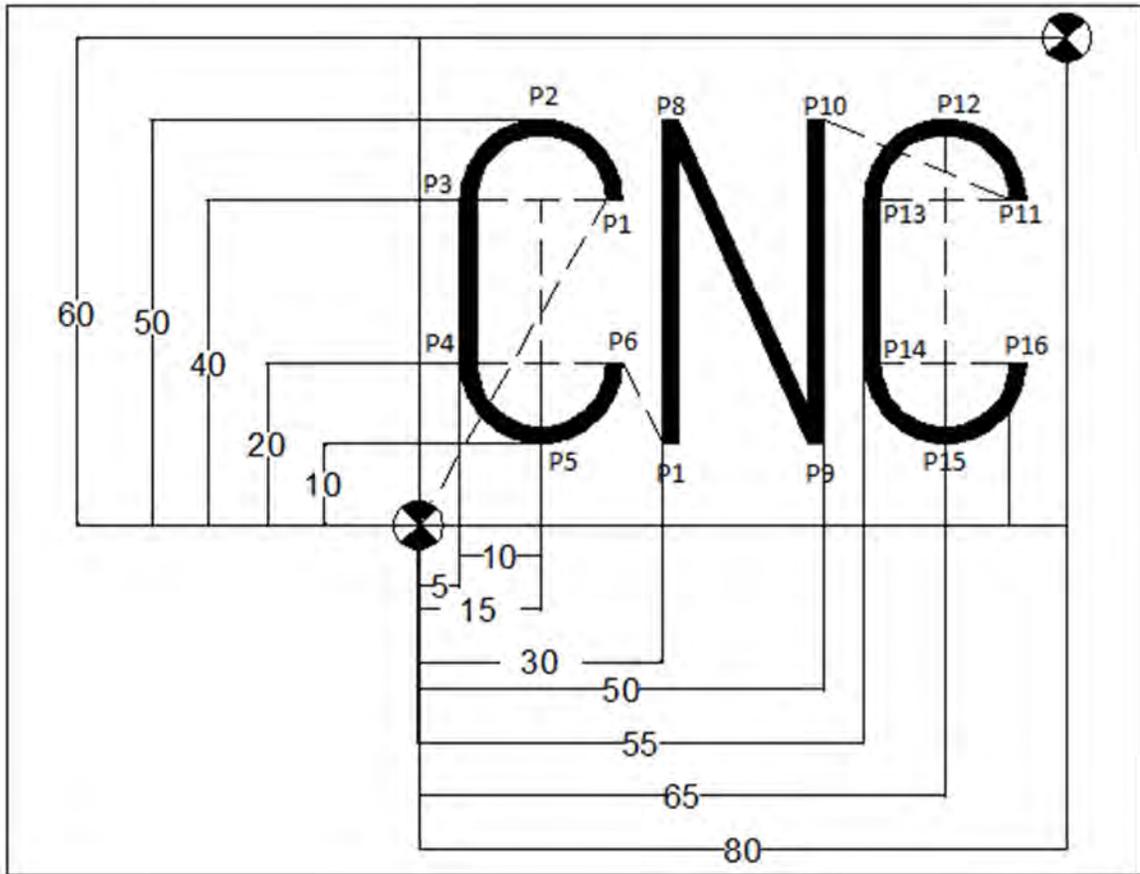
Pieza Que Se Elaborará En La Fresadora Cnc
